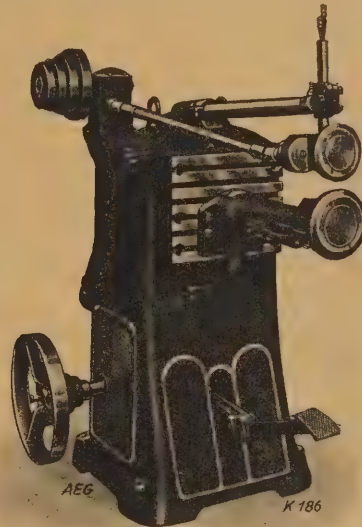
Rundnahtschweißmaschine zum Verschweißen von Bändern im fortlaufenden Zug. Leistung 15 kVA.
